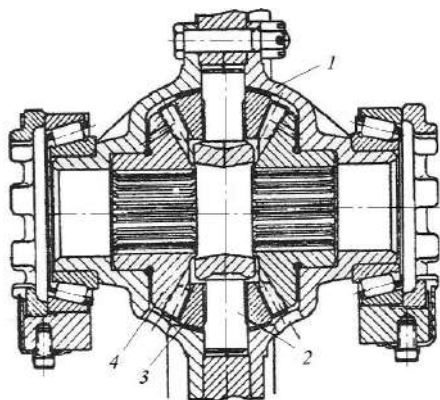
Конічний диференціал: 1 – корпус; 2 – вісь сателітів; 3 – конічний сателіт; 4 – півосьова шестерня
